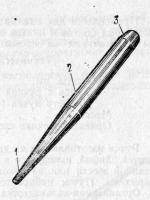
1 — конусная часть; 2 - корпус; 3 - ударная часть
